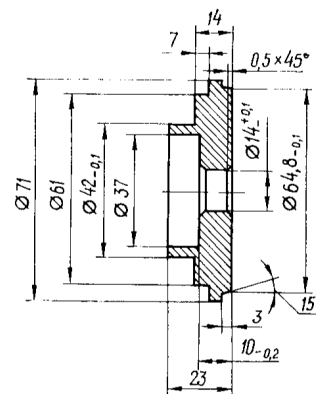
Оправка для запрессовки внутренних подшипников колесного редуктора
